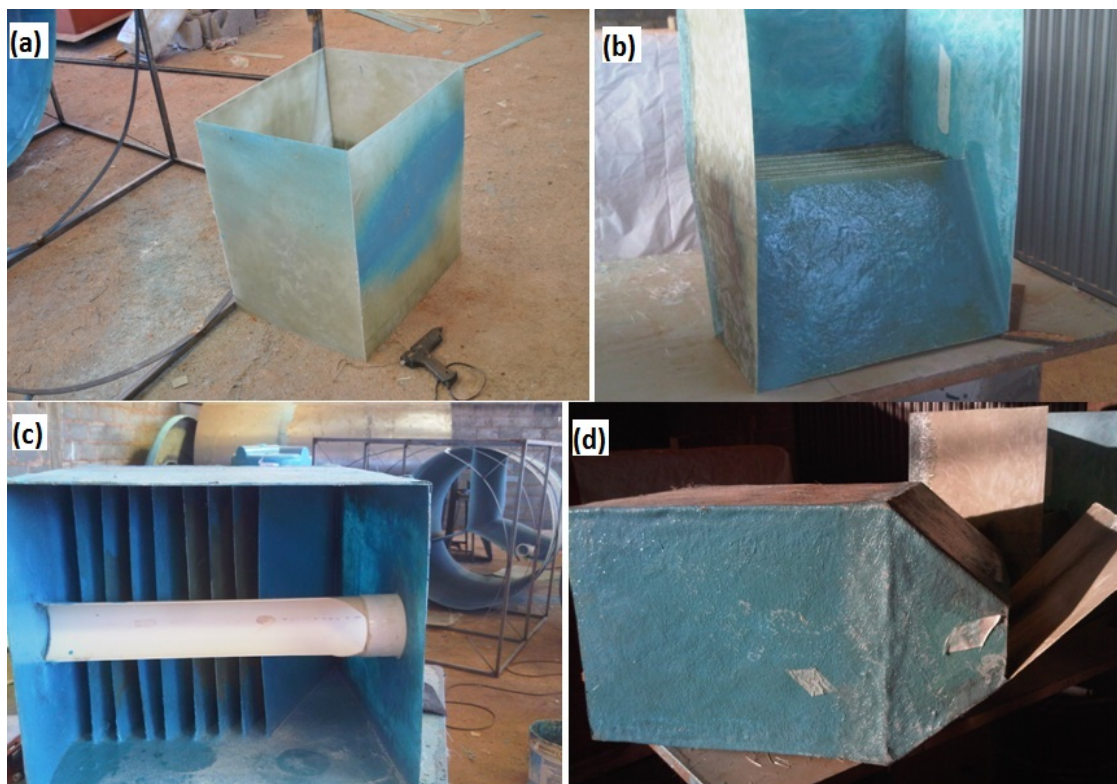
(a) Desenho da vista do topo do protótipo. (b) Vista da câmara 1 – T.I.M. Tanque Imhoff Modificado. (c) Vista câmara 2- F.A.1, Filtro Anaeróbio 1; (d) Vista da câmara 3 – F.A.2 + D.L.S, Filtro anaeróbio 2 e Decantador Laminar Secundário.
